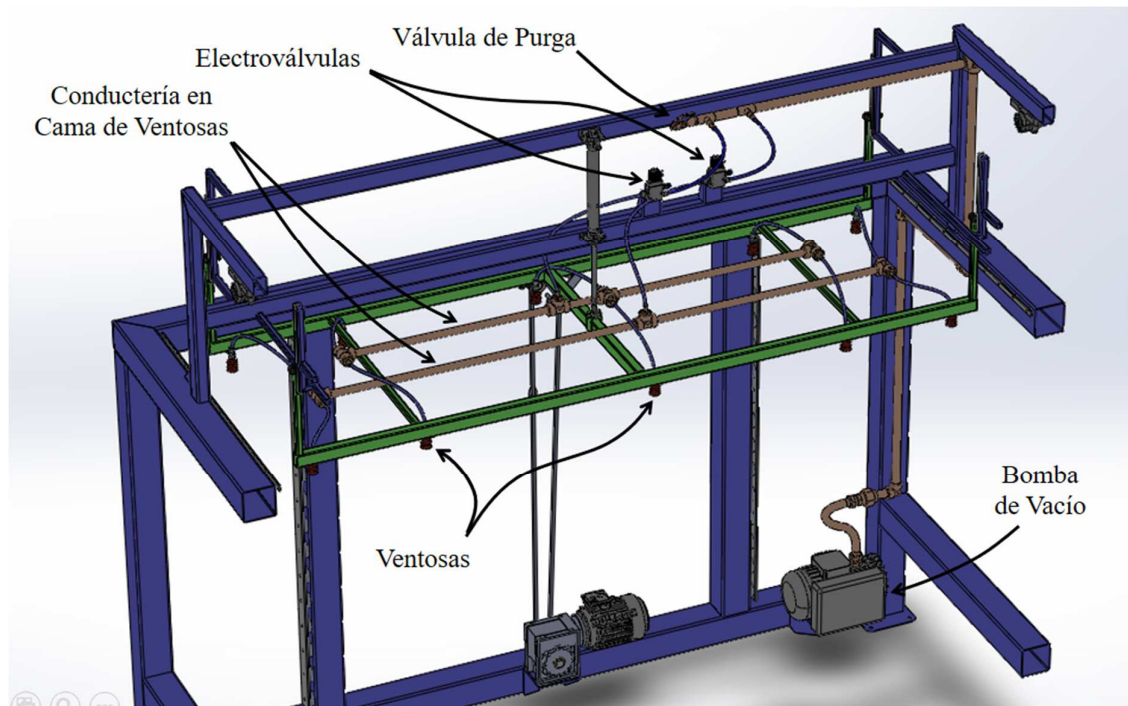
Conductería del Sistema de Succión (resaltada en verde).
